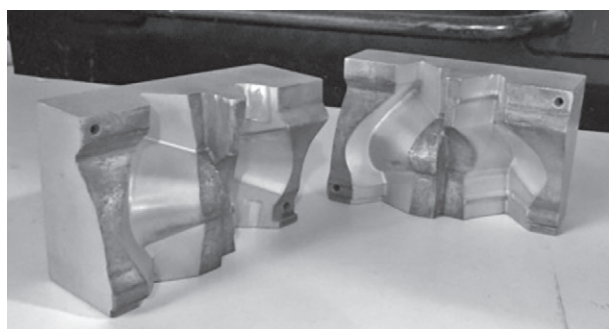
Стержевая оснастка для производства отливки «Реактор 3301709155»
